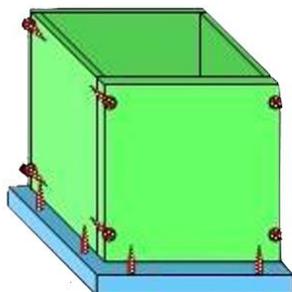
Attachez les parois du coffret les unes aux autres au fond de la boîte
